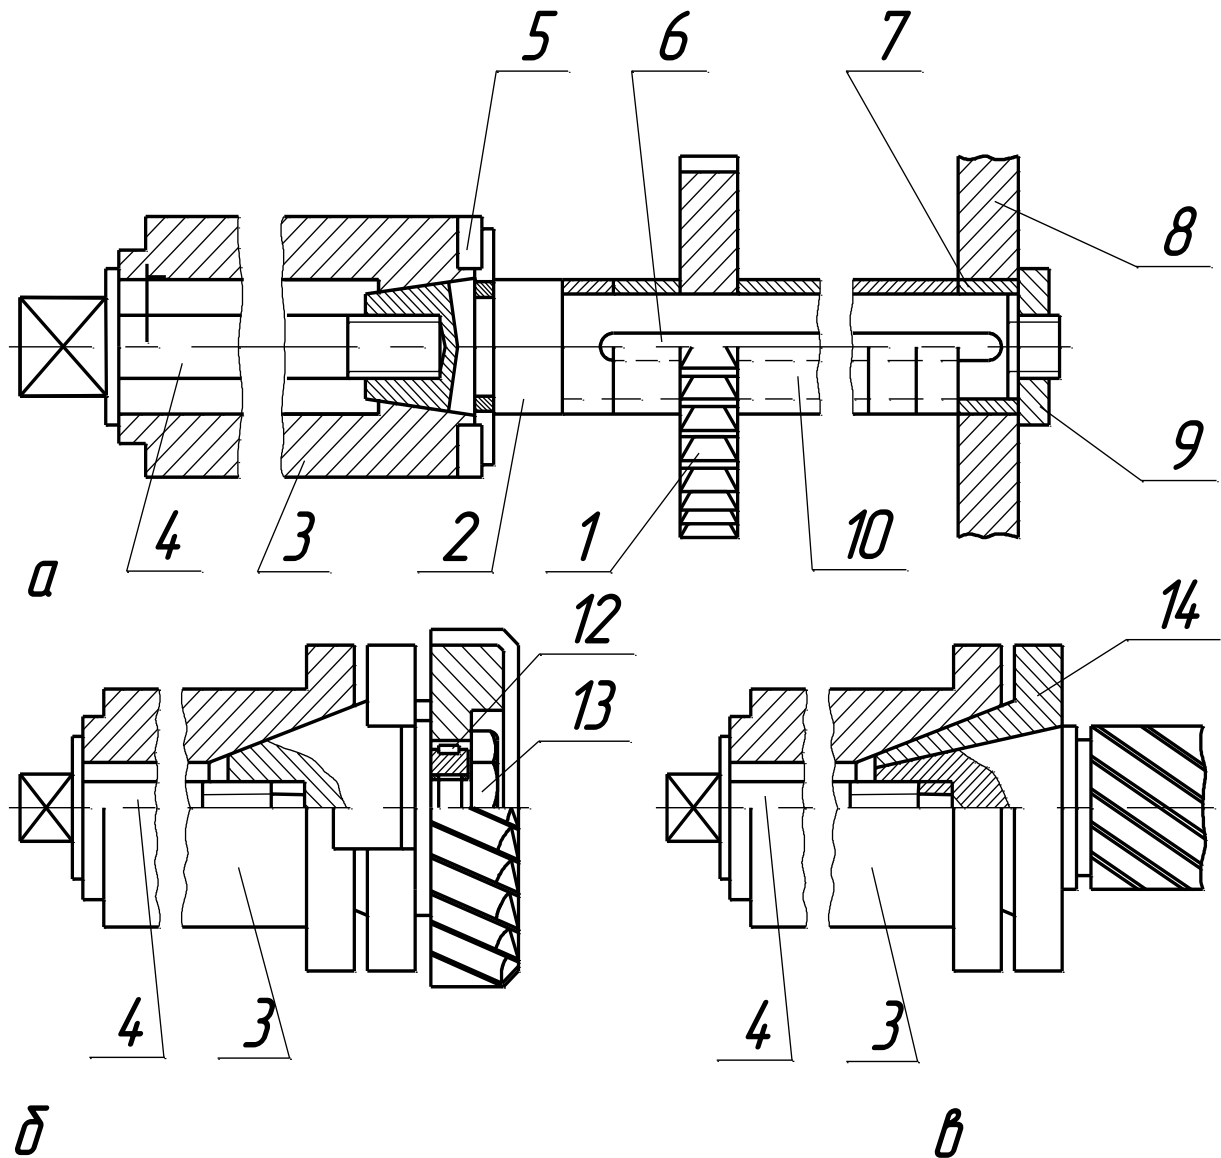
Схеми кріплення інструмента на фрезерних верстатах
